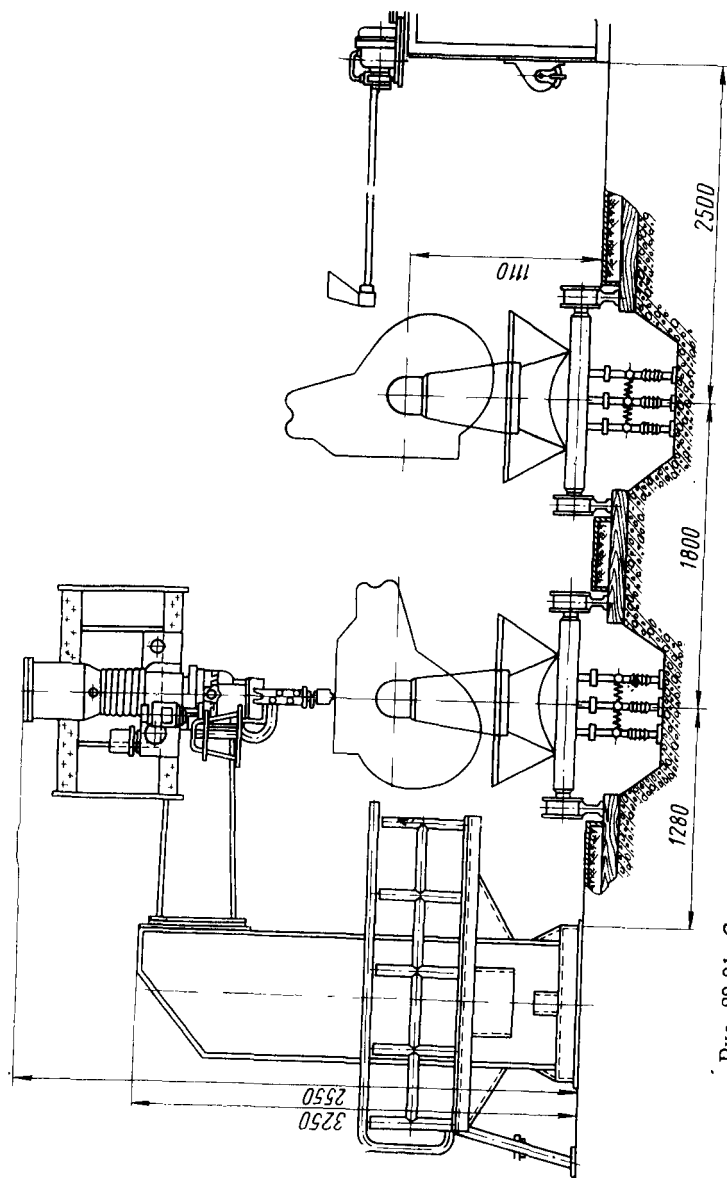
Сварка коробки бортовых фрикционов в линии тележечного конвейера
